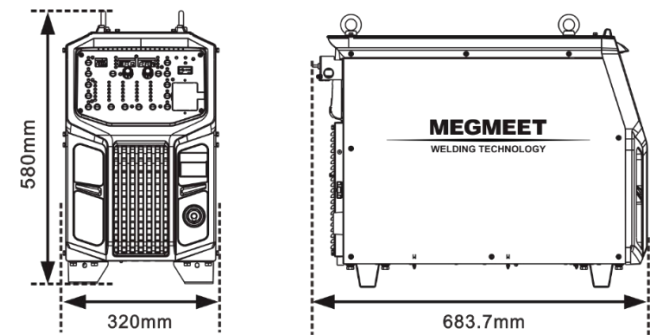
Ehave 2 PM400/500A 系列焊接电源外观及尺寸（单位：mm）
